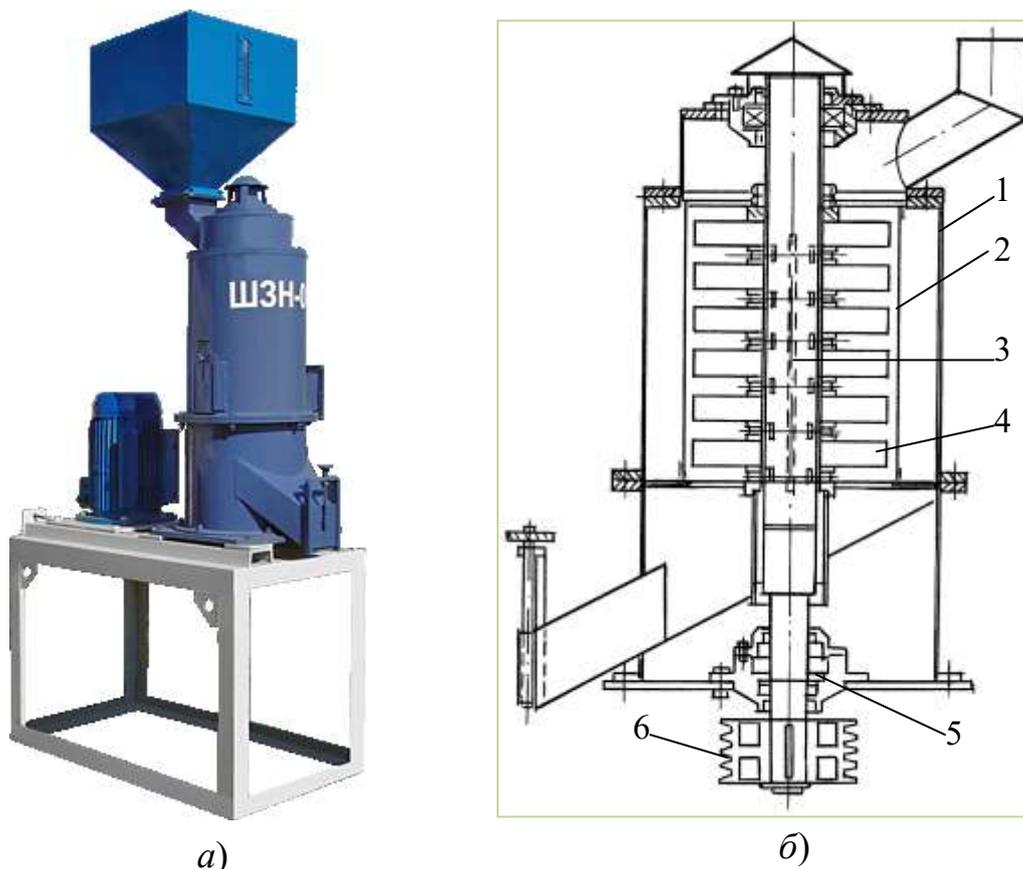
Установка для шелушения зерна ШЗ-01 (ШЗН-01):
